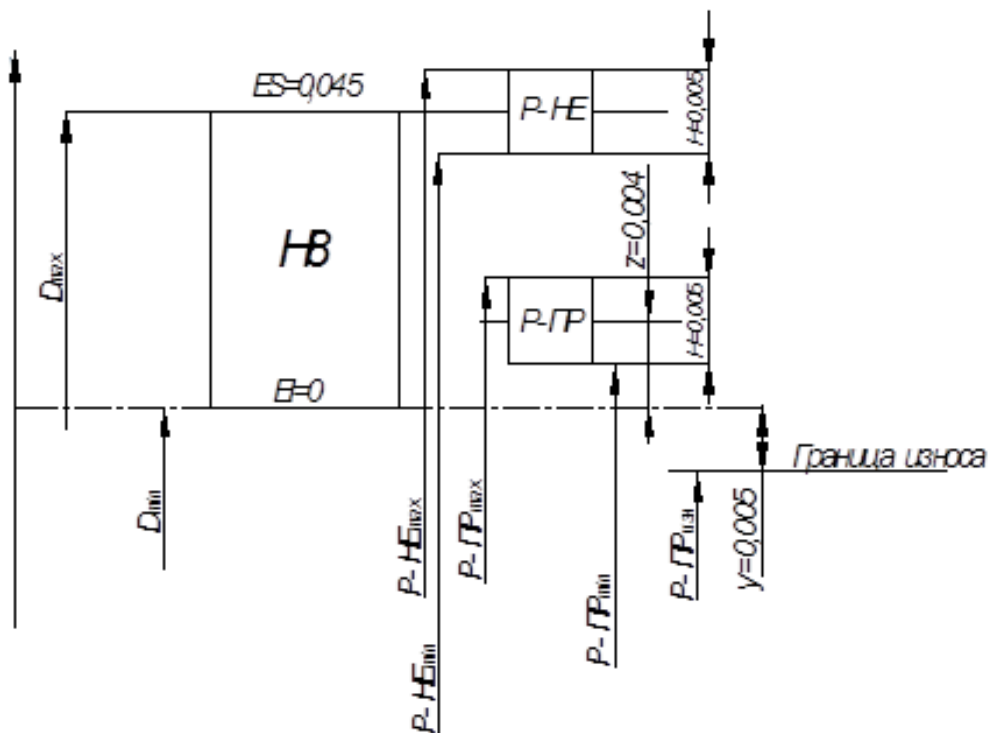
Схема полей допусков калибра-пробки
